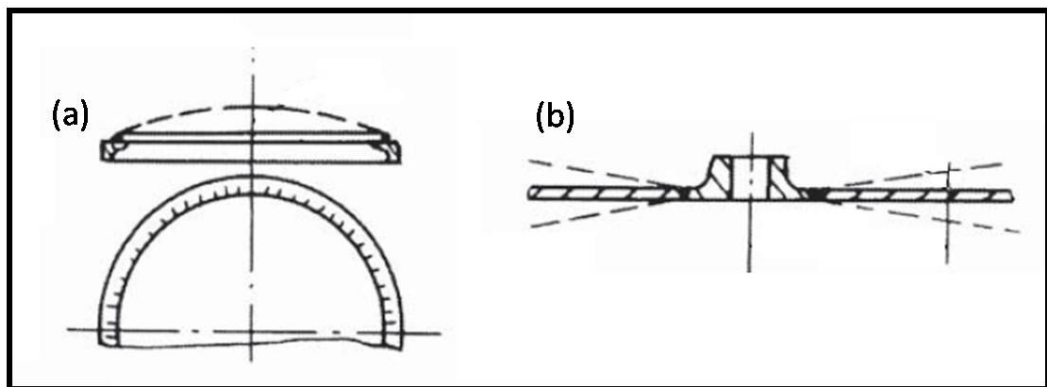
Patrones de distorsión por pandeo generados por soldaduras circulares [15]
